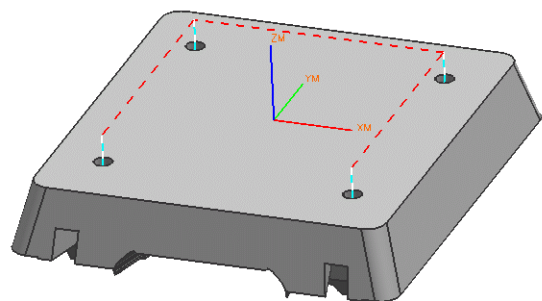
Vložka- prvá strana- operácia face milling area- 10V
